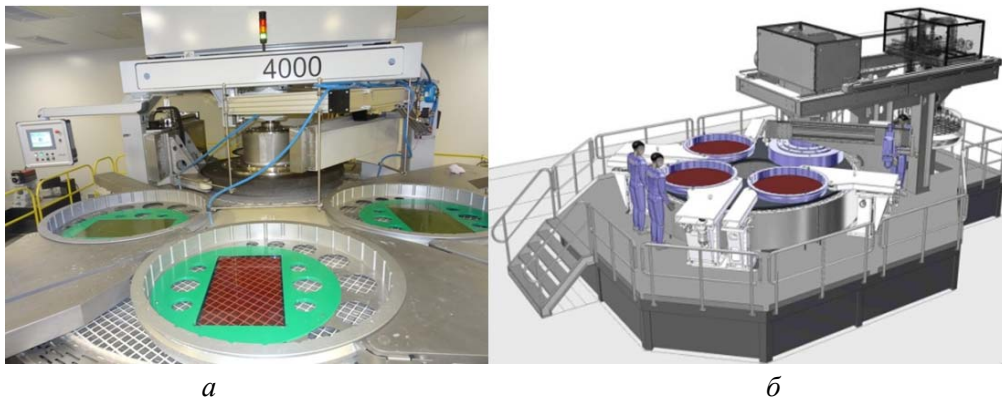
Процесс обработки крупногабаритных оптических деталей полноразмерным инструментом методом свободного притира на станке FLP-4000: а) фотография процесса обработки в конструкциях сепараторного типа; б) общий вид станка с зонами обработки крупногабаритных оптических деталей.
